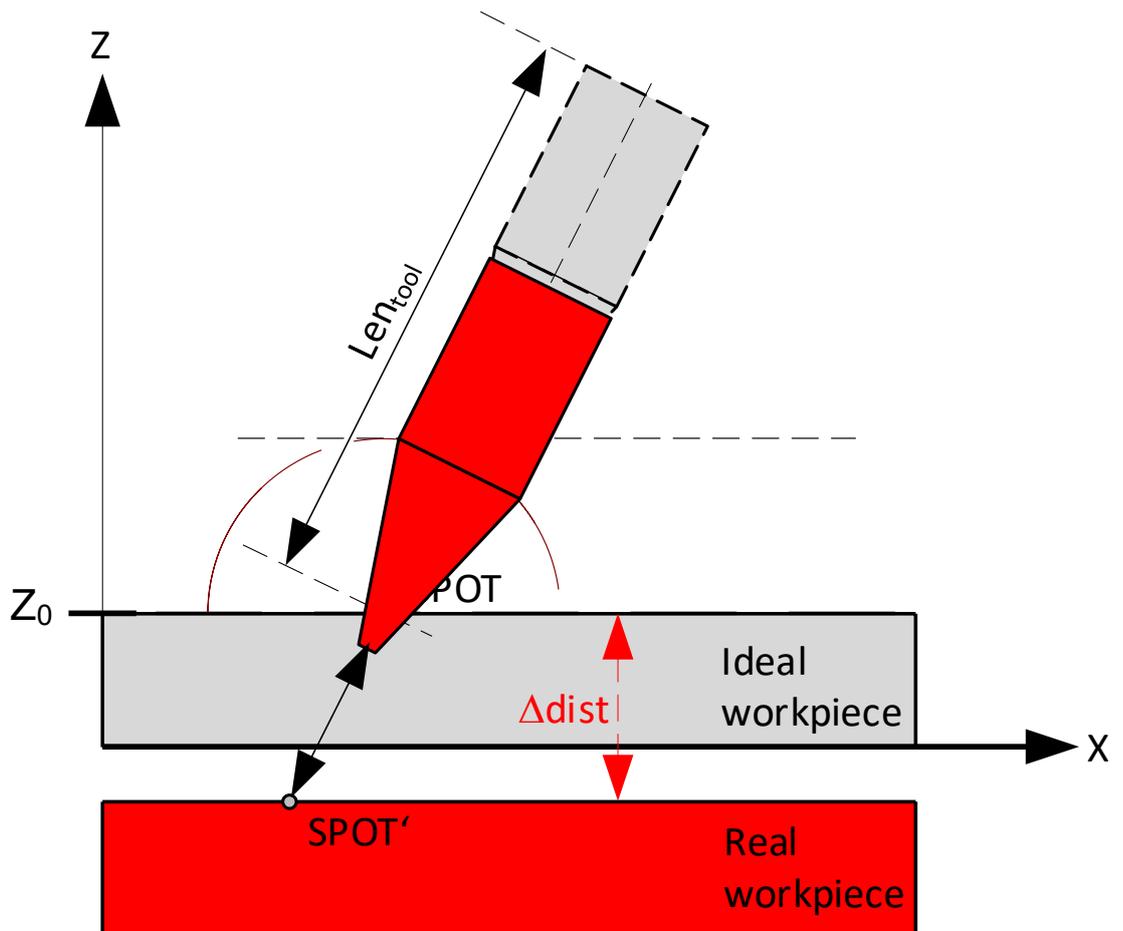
Ausgleich der Abweichung in Werkzeugrichtung
